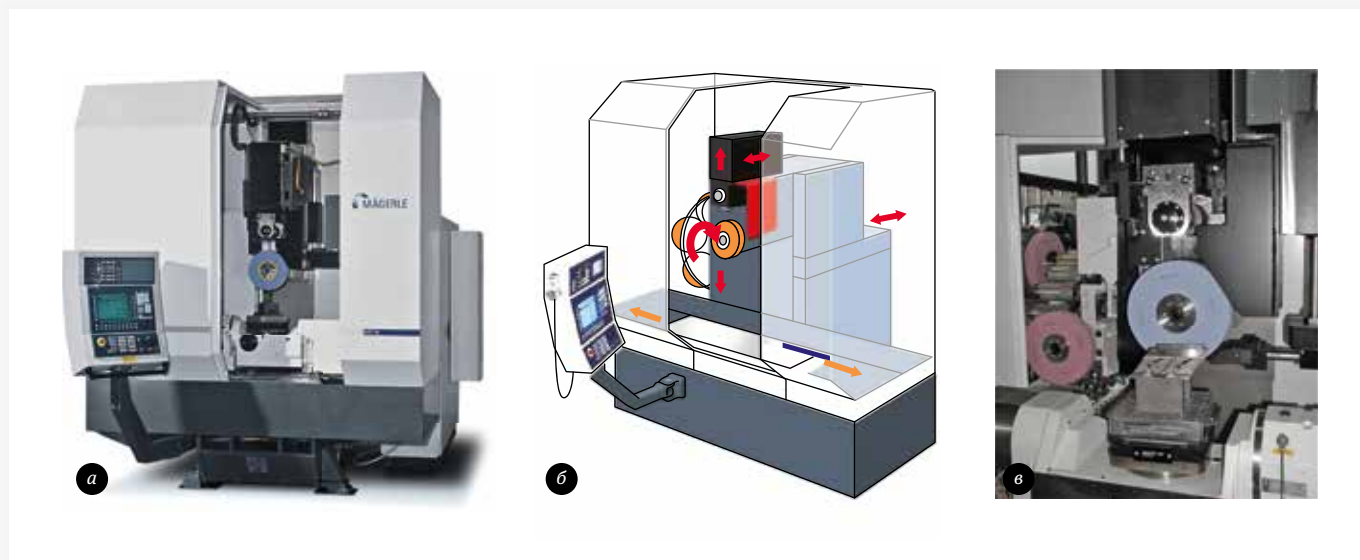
Профилешлифовальный станок MFP-050.65.65: *а* – общий вид; *б* – схема 5-осевой обработки и зоны шлифования; *в* – схема непрерывной правки алмазным роликом и автоматической смены шлифовальных кругов для профильного глубинного шлифования лопаток турбины
